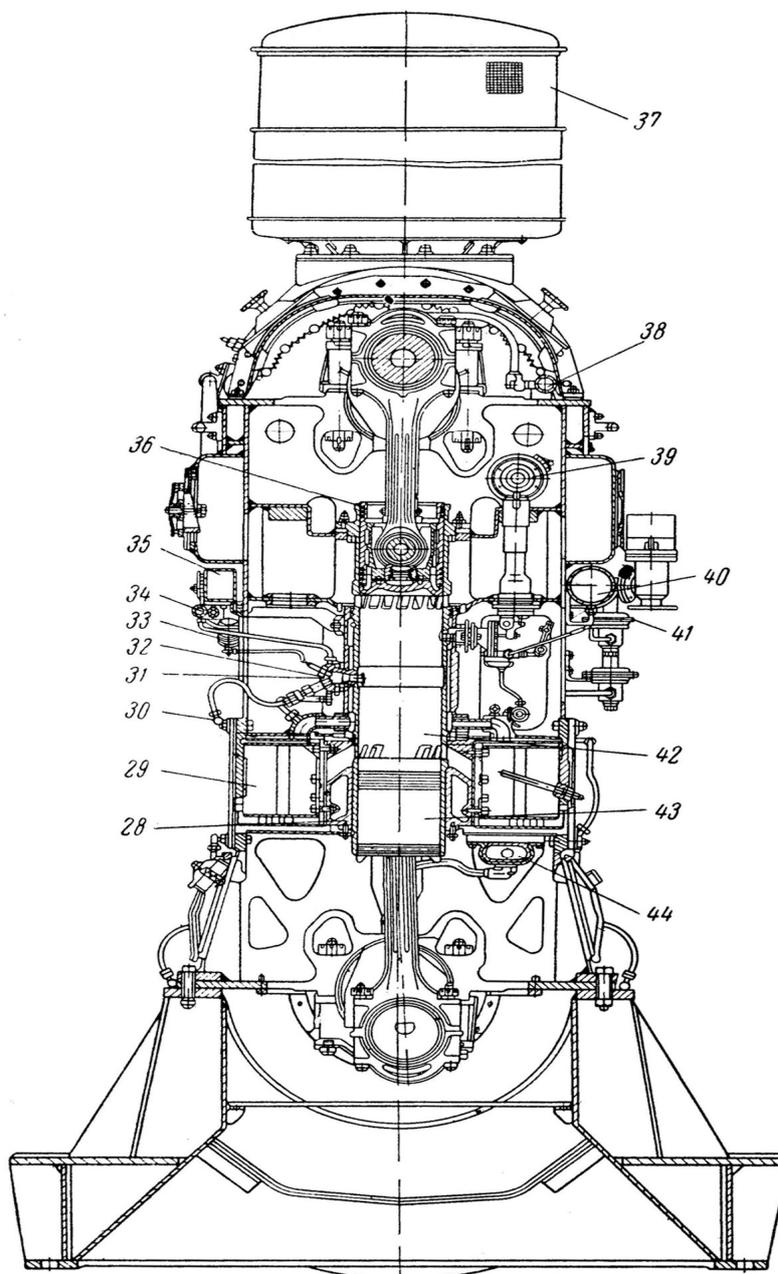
а Газовый двигатель 1ГД100. Поперечный разрез [6]
